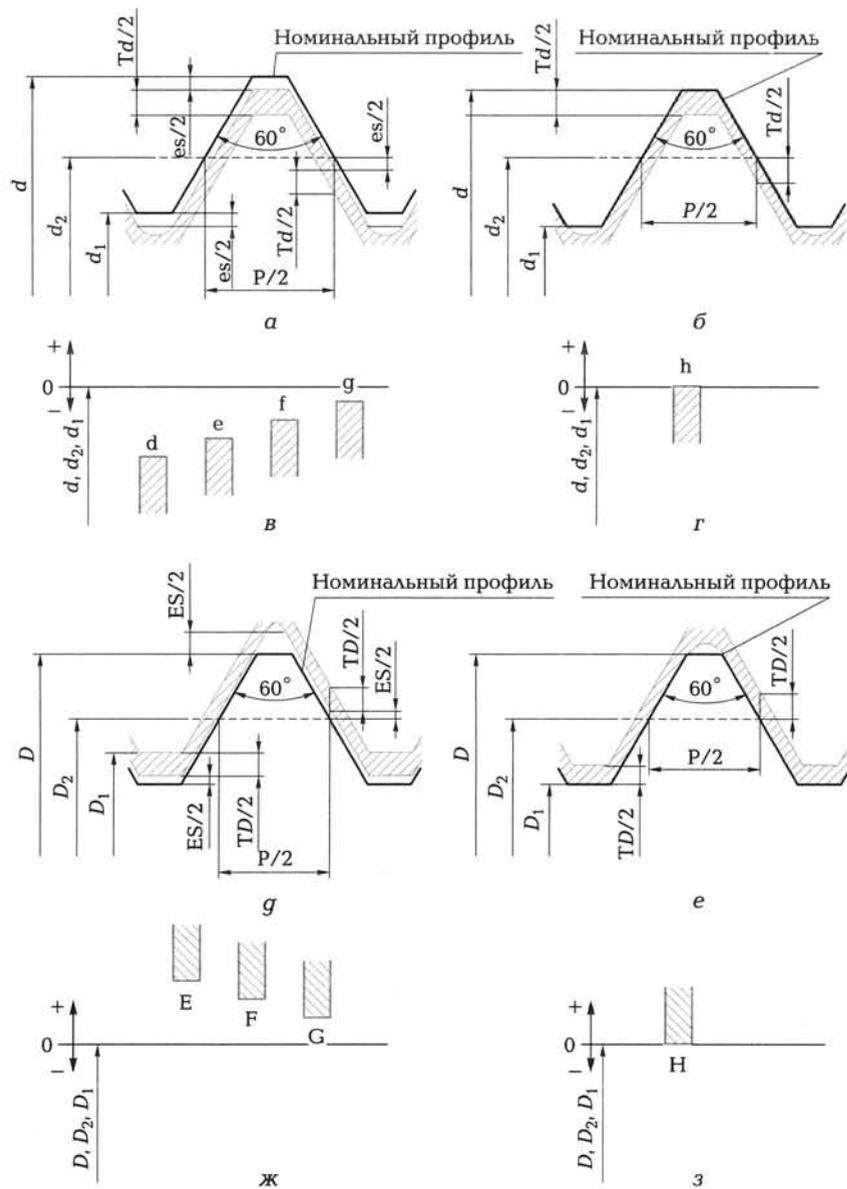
Расположение полей допусков метрической резьбы при посадках с зазором:
